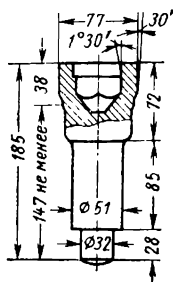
Однопереходная штамповка поковки со ступенчатым стержнем и полкой головки
